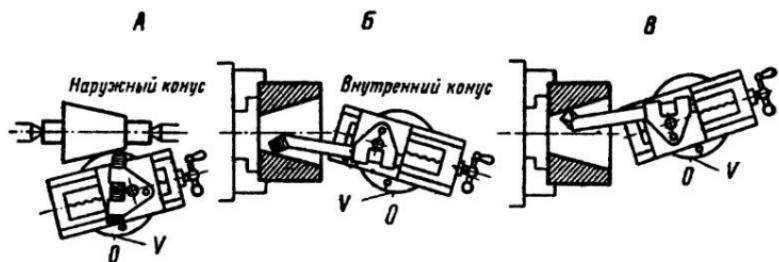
Обработка наружного и внутреннего конусов на токарном станке: V — величина смещения верхних салазок суппорта относительно его поперечных салазок (угол поворота).
